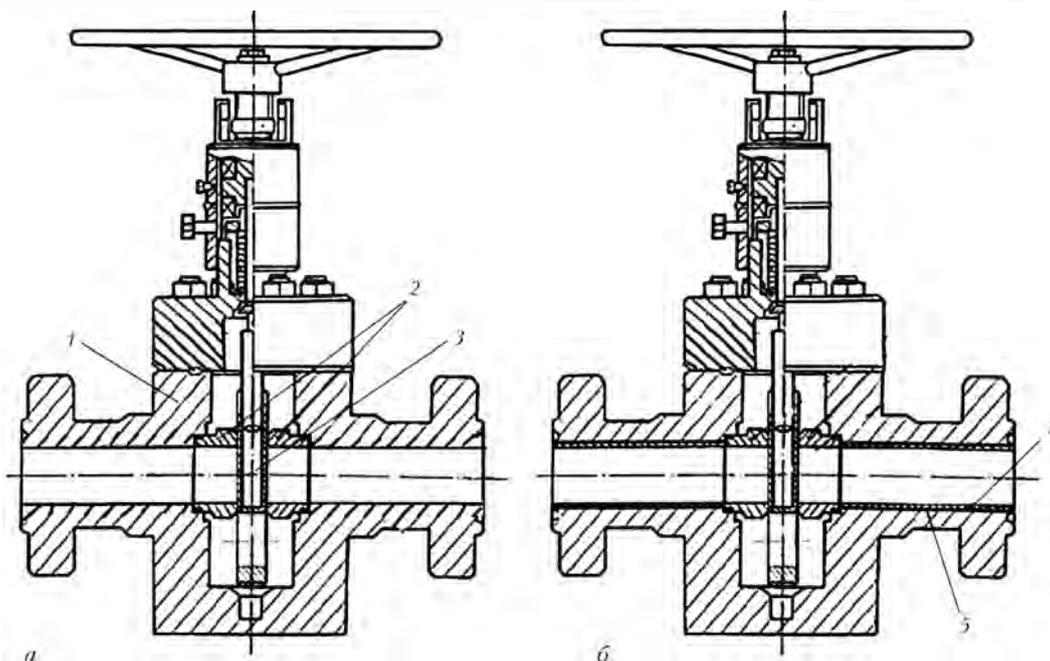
Схема фланцевой задвижки высокого давления с цельнолитым электрошлаковым (а) и композиционным (б) корпусом: 1 – корпус; 2 – седла; 3 – штибель; 4 – коррозионно-стойкое покрытие канала; 5 – паяный шов
